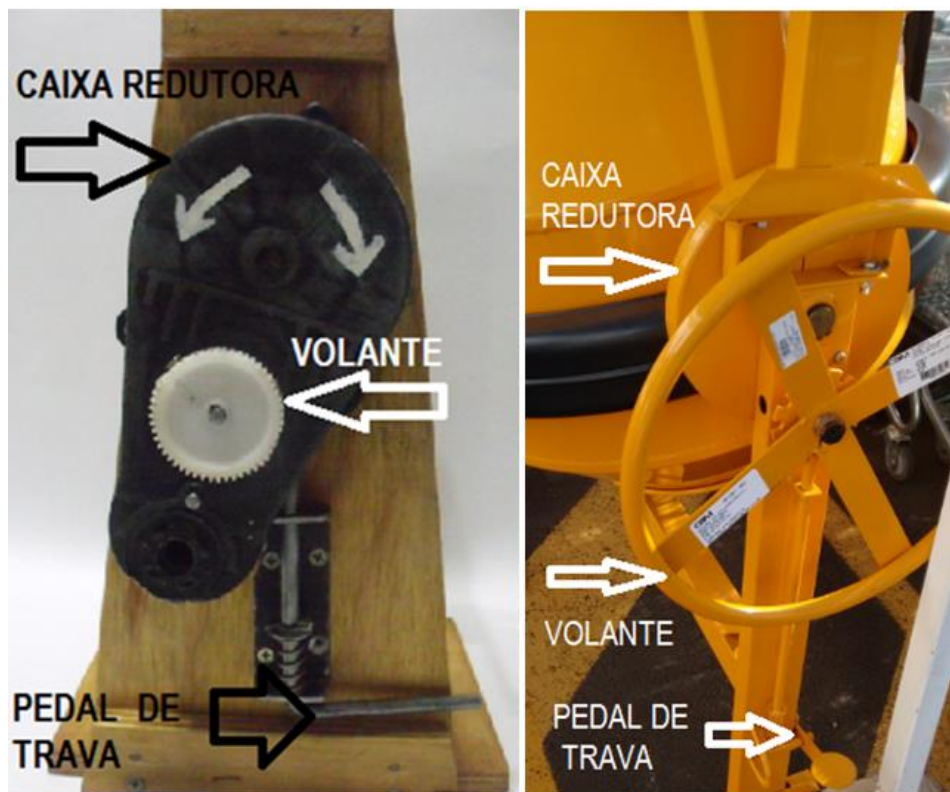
Sistema de trava posicionado entre dentes da engrenagem.
